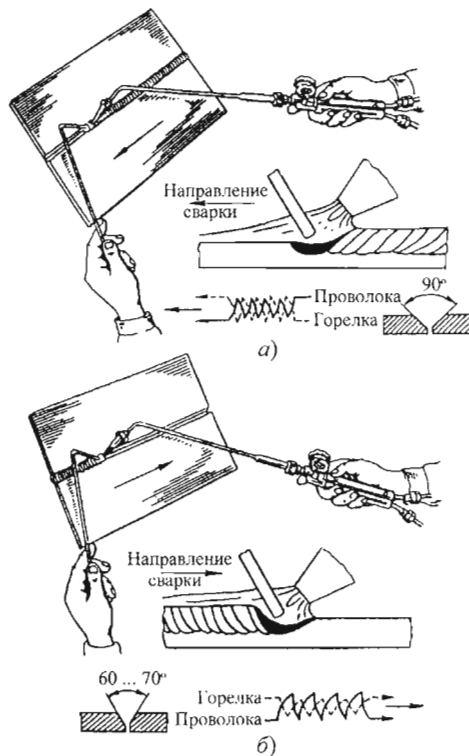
Схемы левого (а) и правого (б) способов сварки
